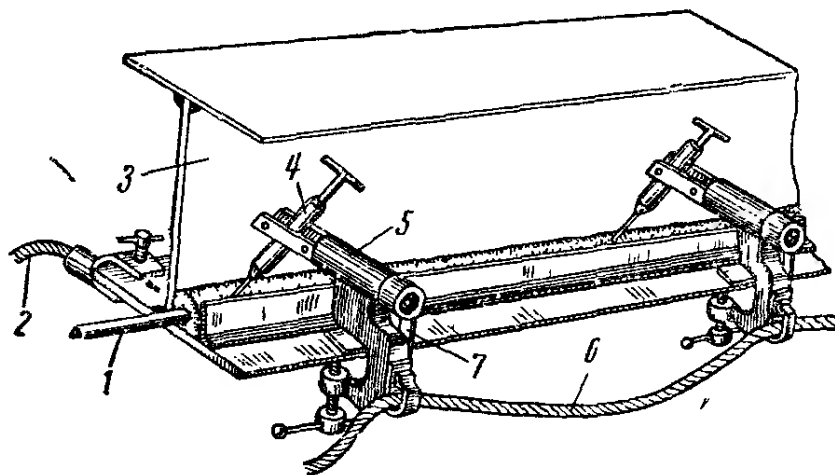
Сварка швов двутавровой балки лежащим электродом под флюсом:
